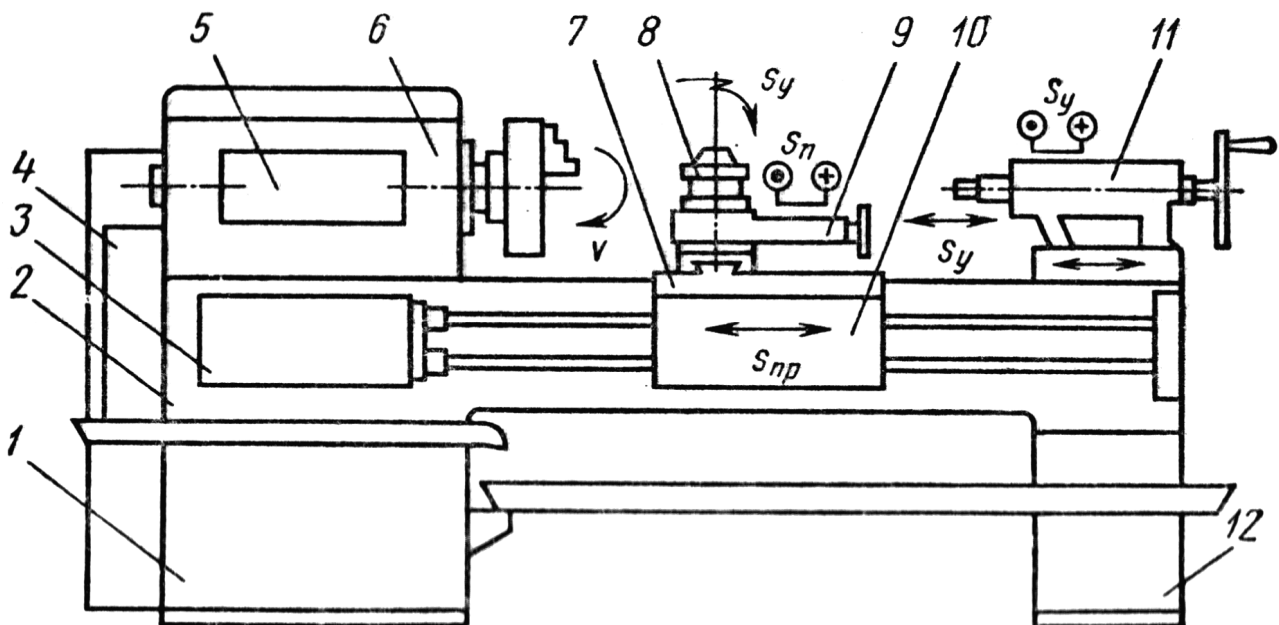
Загальний вигляд токарно-гвинторізного верстату
